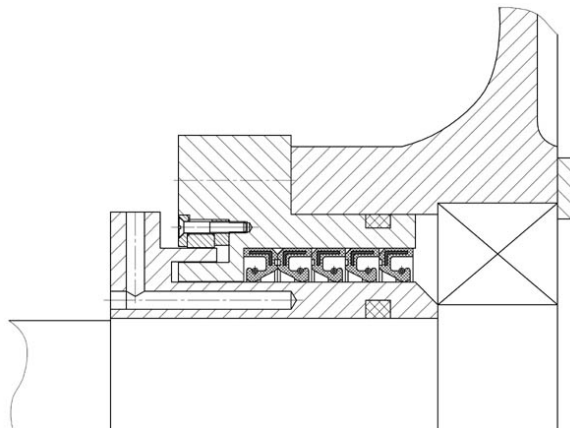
МЖГ подшипникового узла барабана сепаратора
